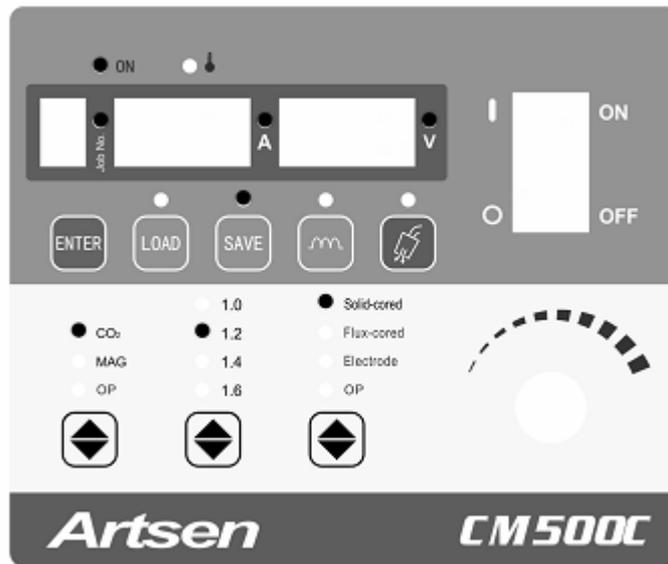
Загрузка параметров режима сварки
